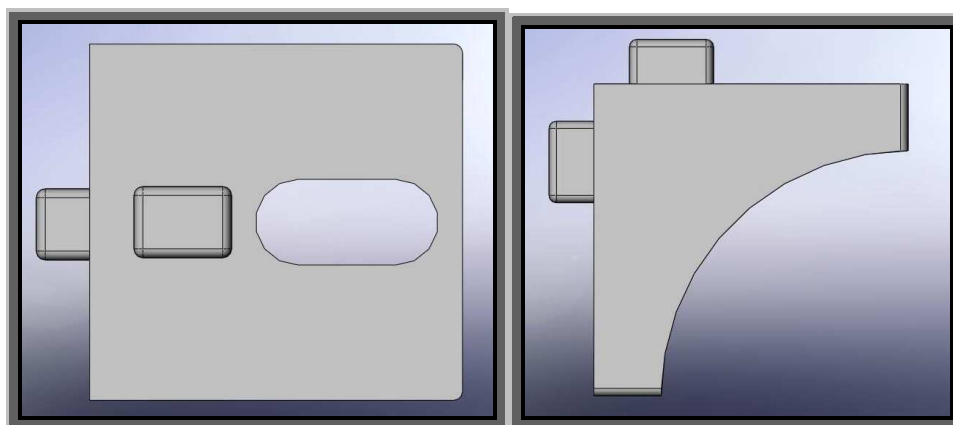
Vista isométrica del cuerpo del deslizador.
